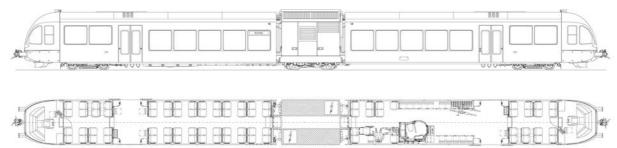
Dessin d'ensemble du GTW DMU-2 2/6 de la STA.<sup>50</sup>
